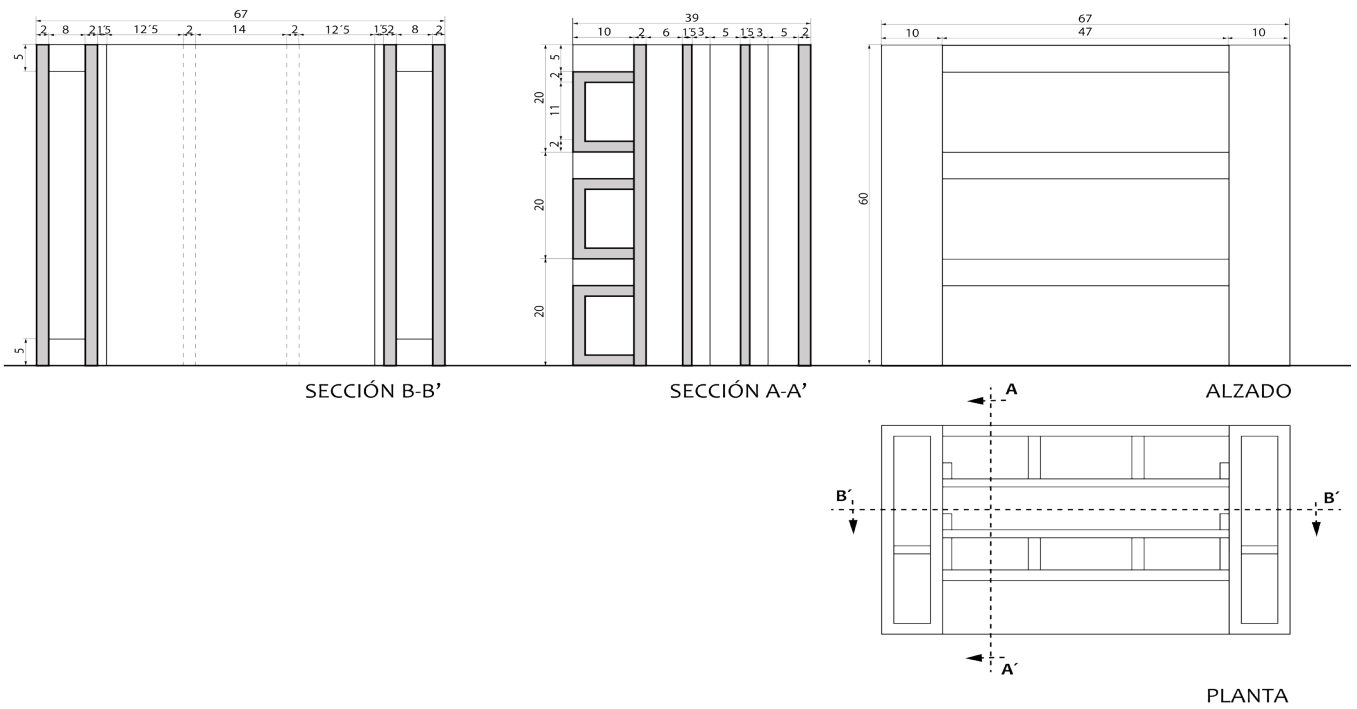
Módulo tipo del prisma A y C. Planta, alzado y secciones
